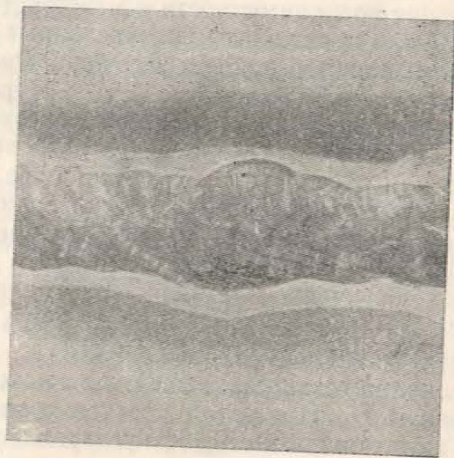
Коррозия вблизи сварного шва после электродуговой сварки стали 18-8 при травлении в смеси азотной и плавиковой кислот. $\times 2$
